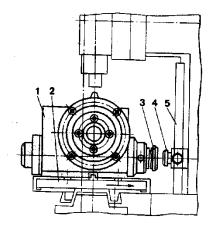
Стойка поворотно-делительная 1 - приспособление, 2 - стол станка, 3 - шток, 4 - упор, 5 - стойка
